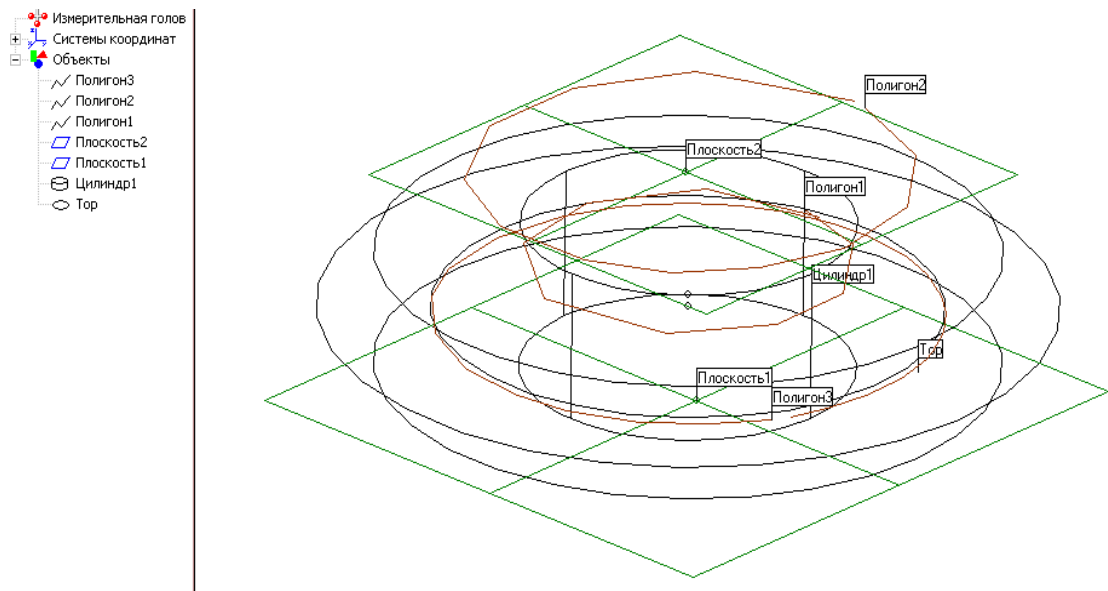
Вимірювання поверхонь кільця підшипника кочення
